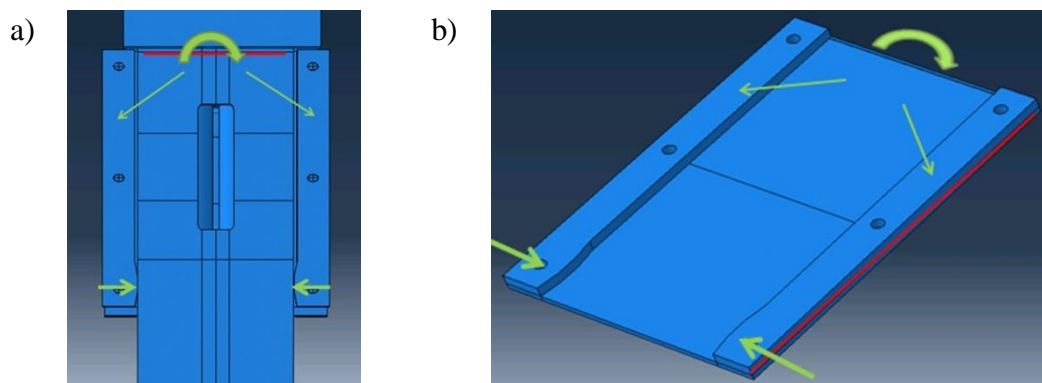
Cheminement des efforts à travers la plaque extérieure a) Vue éclatée sans plaque
